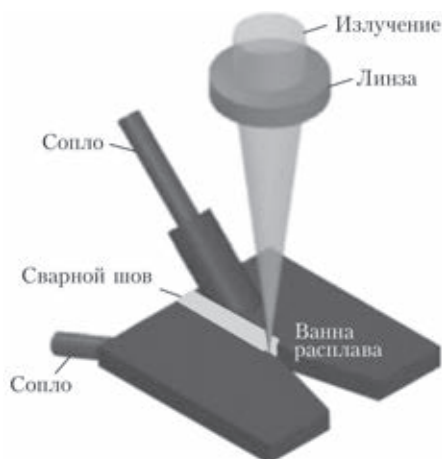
Технологическая схема лазерной сварки алюминиевых сплавов
